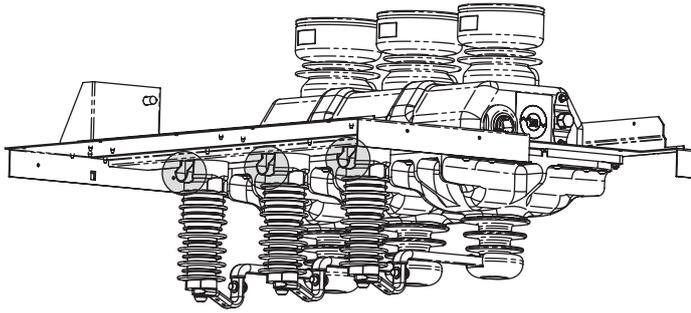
Terminales del seccionador para las conexiones en cable del indicador de tensión
